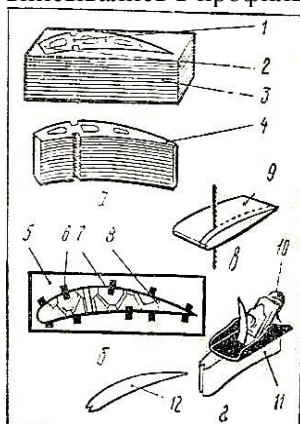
Способы изготовления нервюр а—вырезанием из шпона по шаблону; б—выклеиванием из реек; в—выпиливанием профилированной заготовки; г—строганием профилированной заготовки; 1—шаблон; 2—гвоздь; 3—полоски шпона в блоке; 4—блок вырезанных нервюр; 5—стапель; 6—упоры; 7—нервюра; 8—подкос; 9—профилированная заготовка; 10—рубанок; 11—строгаемая заготовка; 12—заготовка нервюры
